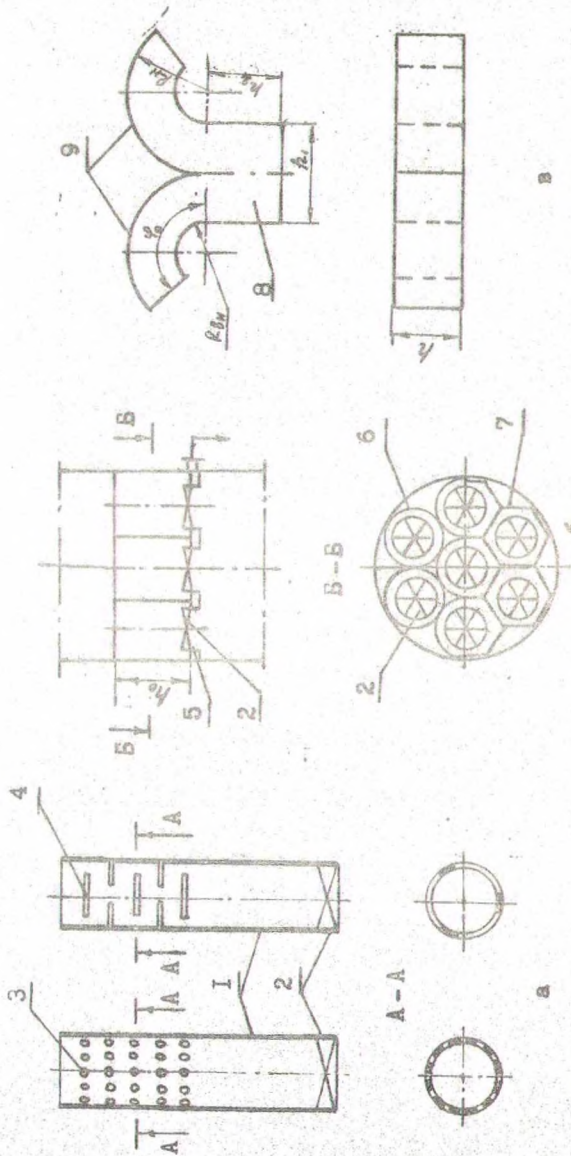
Сепарационные устройства. а, б - элементного типа, в - с кризольными каналами. 1 - цилиндрический патрубков; 2 - зажиматель; 3 - круглые отверстия; 4 - щели; 5 - стакан; 6 - шестиугольный патрубков; 7 - шестиугольный патрубков; 8 - входной патрубков; 9 - кризольные каналы.
